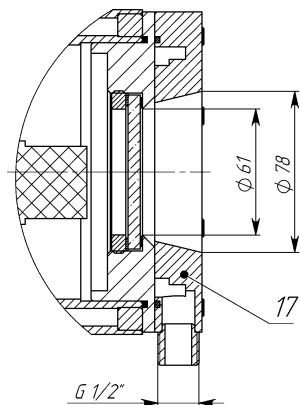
Внешний вид термокожуха ТВК-07-В с установленной блендой (БЗП)
